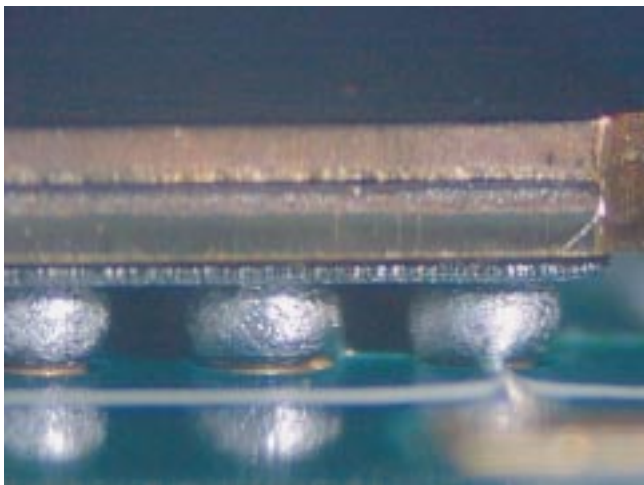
Soldadura SnPb; Proceso No-Lavable
